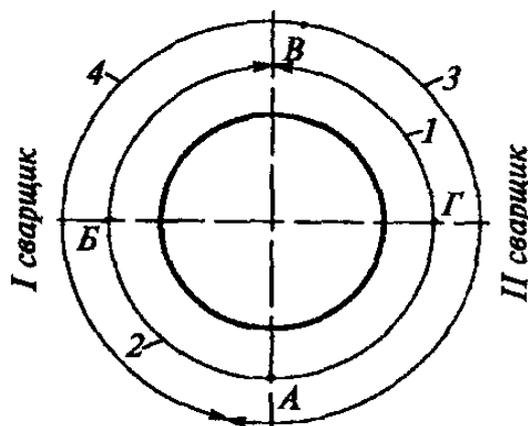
Порядок наложения слоев шва при сварке вертикального неповоротного стыка труб двумя сварщиками.
